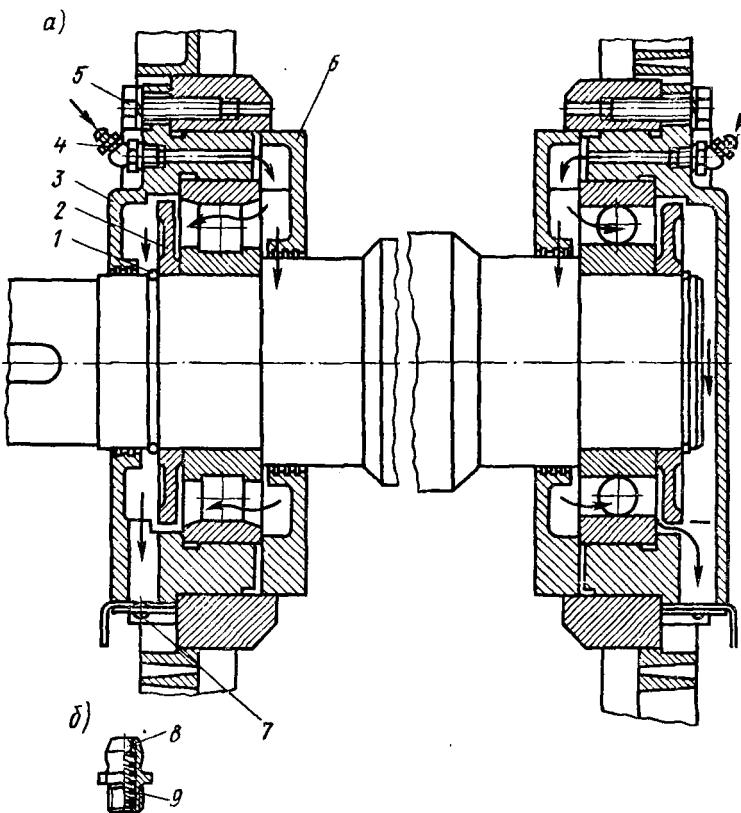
Конструкция подшипникового узла с устройством для пополнения смазки без разборки двигателя (а) и пресс-масленка (б)
